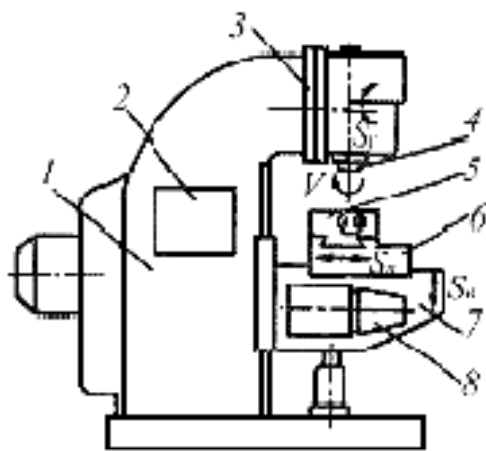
Загальний вигляд вертикально-фрезерного верстата
